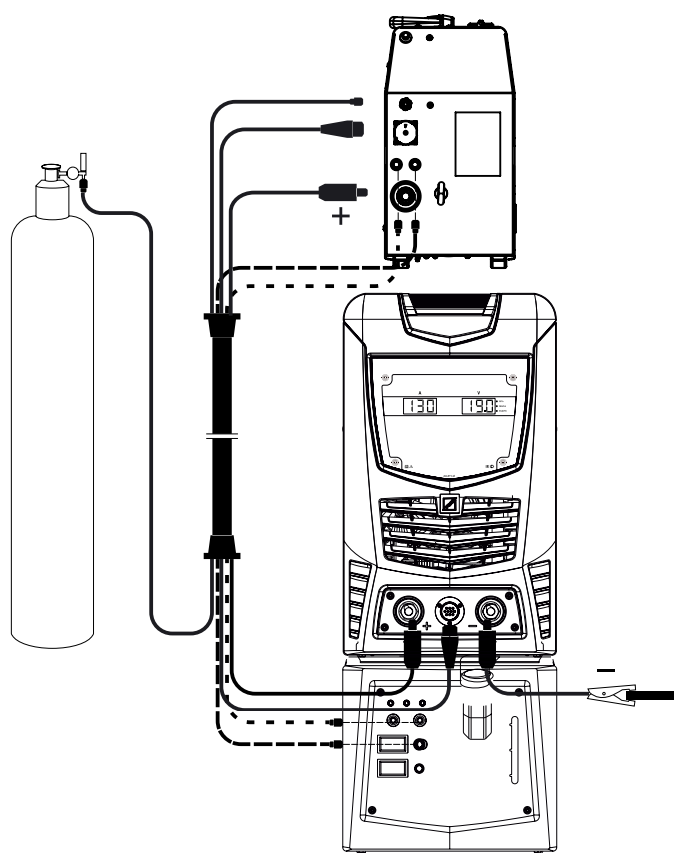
Схема подключения механизма подачи сварочной проволоки
